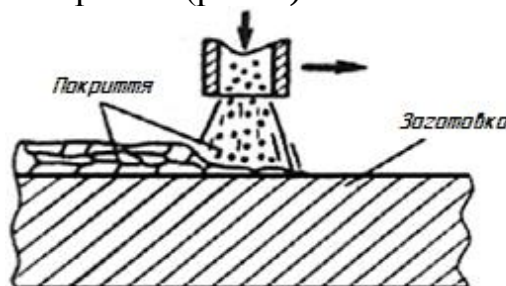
Схема нанесення покриттів. 1-покриття, 2-заготовка
